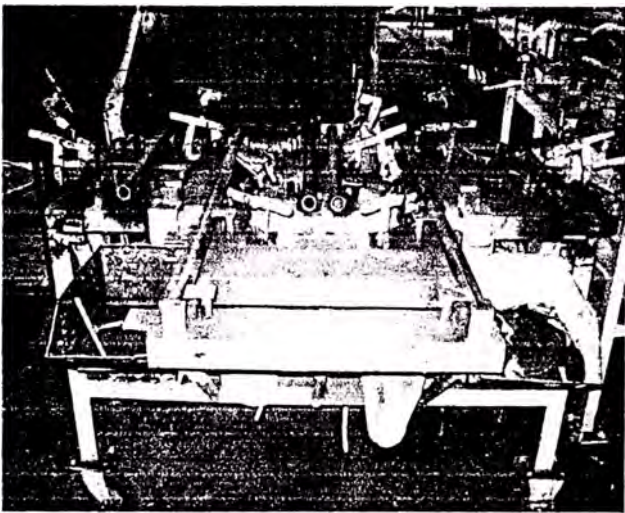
Dispositivo de soldadura neumático preensamble chasis
